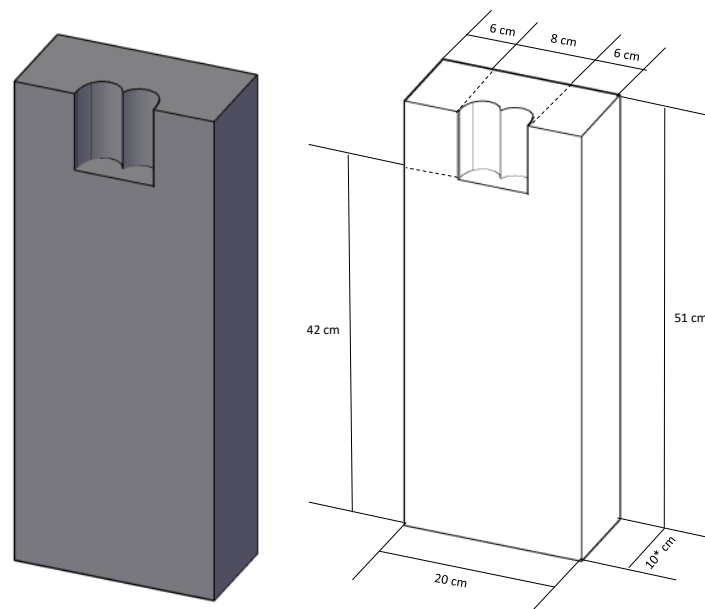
Desenho técnico do suporte final para a rolha, à esquerda, e com as medidas, à direita.
